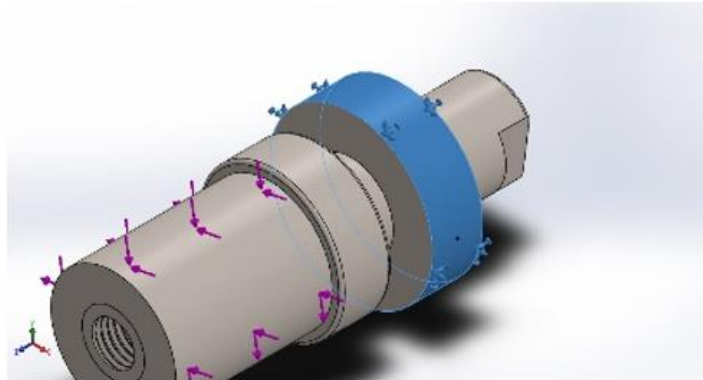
Zona de fixação do conjunto componente e acessórios.
